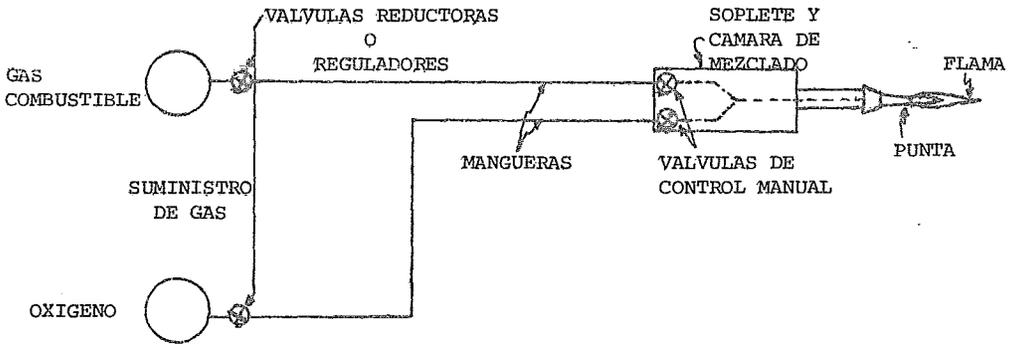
DIAGRAMA ESQUEMATICO DEL SOPLETE Y EL SUMINISTRO DE GAS PARA LA SOLDADURA OXIACETILENICA
